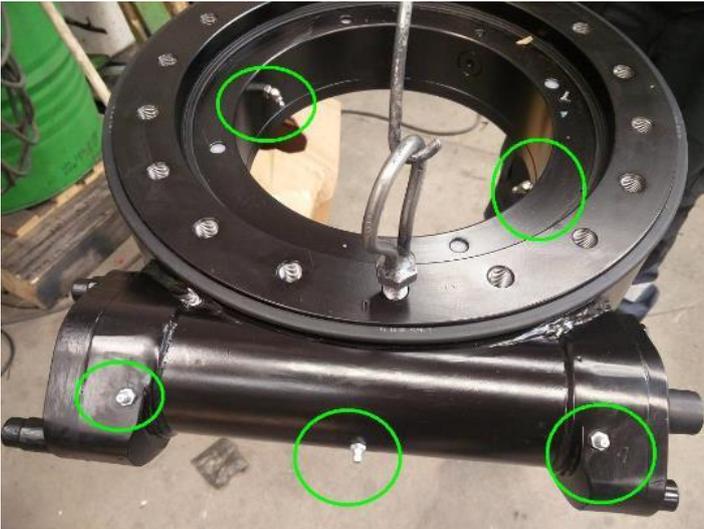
Puntos de engrasado del anillo giratorio. El anillo visto desde abajo.
